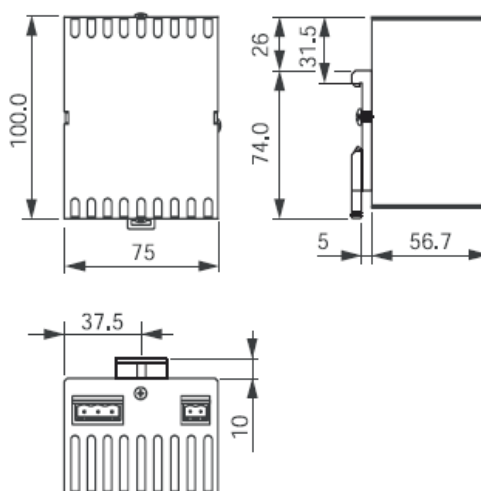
Габаритные размеры блока питания PS24-050D
